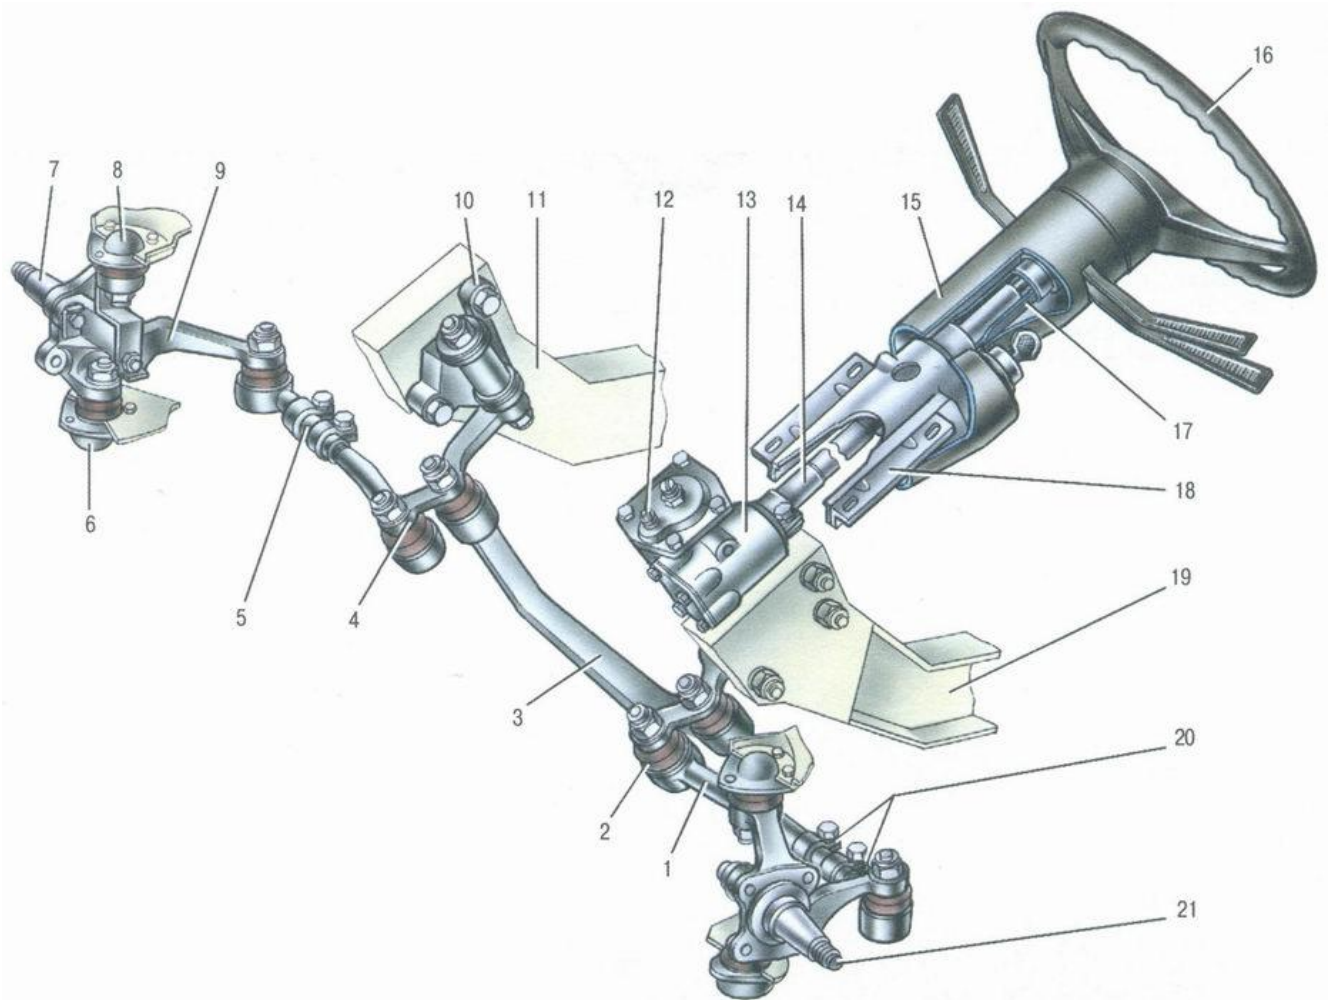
Рульове керування автомобіля ВАЗ 2106: 1 - бічна тяга; 2 - сошка; 3 - середня тяга; 4 - маятниковий важіль; 5 - регулювальна муфта; 6 - нижній кульовий шарнір передньої підвіски; 7 - правий поворотний кулак; 8 - верхній кульовий шарнір передньої підвіски; 9 - правий важіль поворотного кулака; 10 - кронштейн маятникового важеля; 11 - правий лонжерон кузова; 12 - пробка маслоналивного отвору; 13 - картер рульового механізму; 14 - вал рульового керування; 15 - лицувальний кожух вала рульового керування; 16 - рульове колесо; 17 - труба верхньої опори вала рульового керування; 18 - кронштейн вала рульового керування; 19 - лівий лонжерон кузова; 20 - стяжні хомути регулювальної муфти; 21 - лівий поворотний кулак
